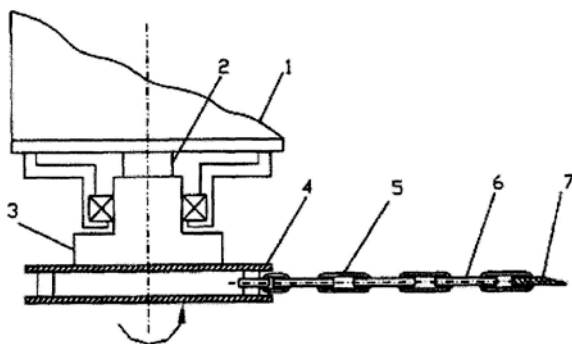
Схема роторного кустореза с гибким рабочим органом: 1 – корпус; 2 – вал; 3 – диск; 4 – оси; 5 – звенья; 6 – измельчающие элементы; 7 – срезающий элемент
